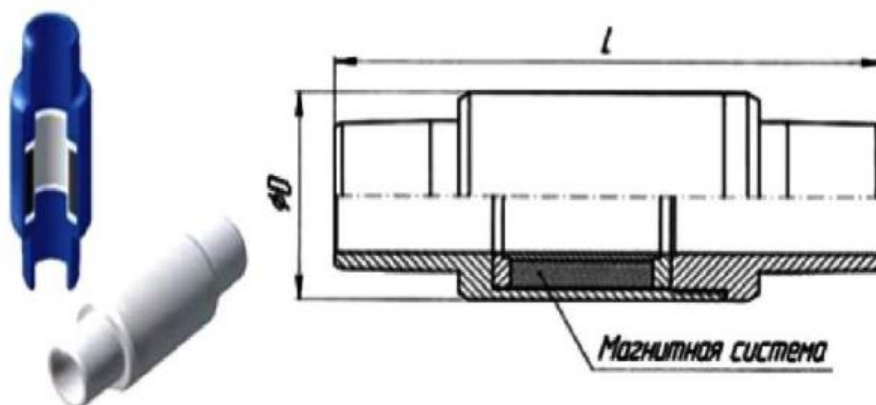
Магнитный активатор Магнитный активатор АМС
